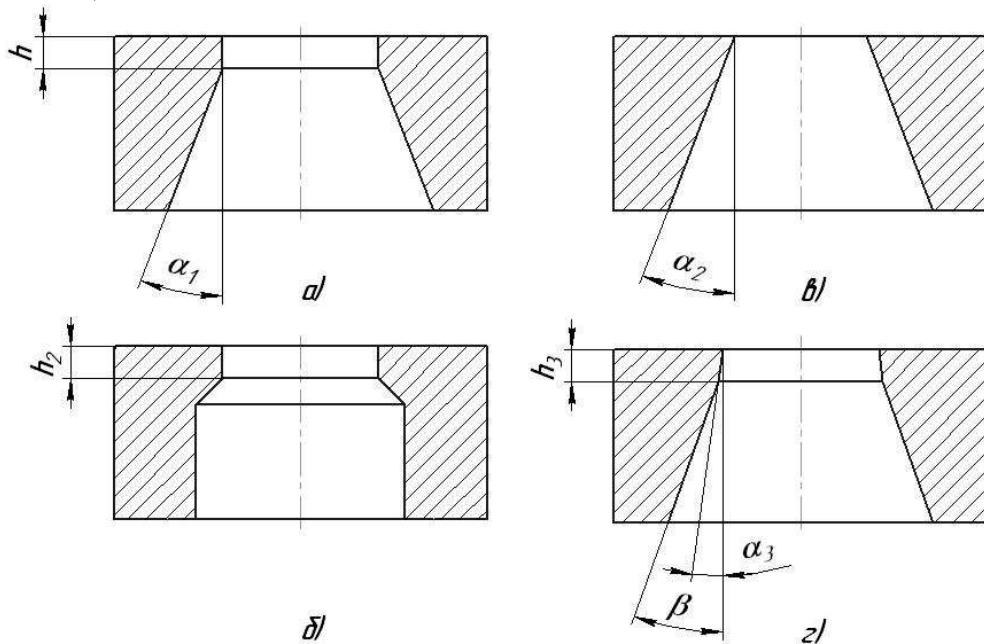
Профіль робочої частини матриці: а – з циліндричним пояском; б – з двома циліндричними ділянками; в – з конусом від робочої (дзеркальної) поверхні; г – з двома конусами
